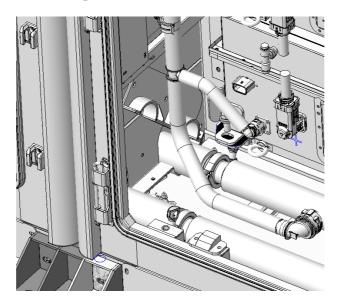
Installazione del tubo flessibile e blocco morsetto
